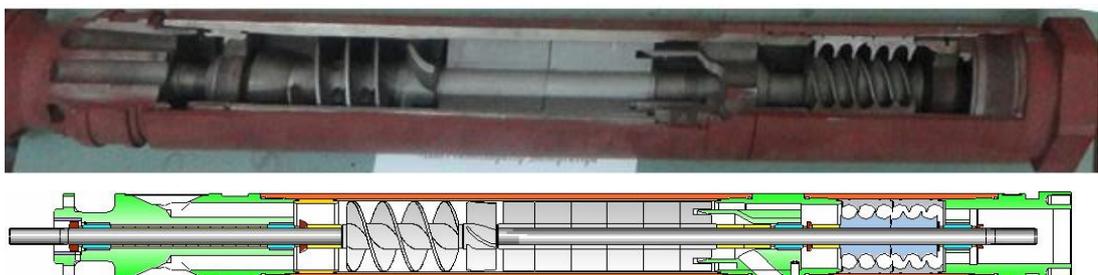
Чертеж и разрез газосепаратора-диспергатора ГДН 5
